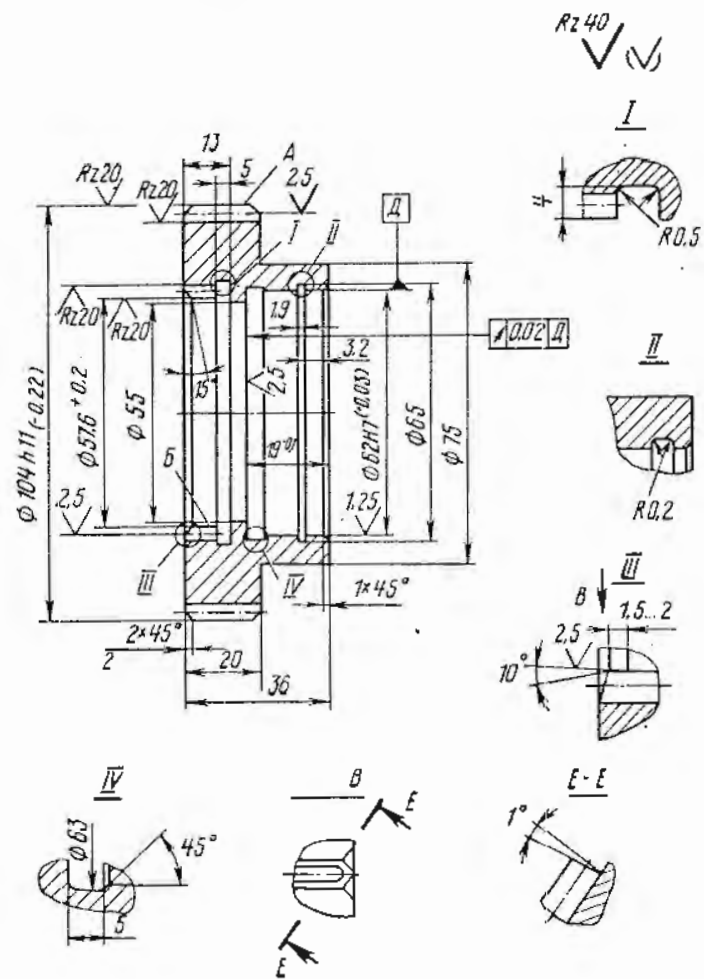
Колесо зубчатое, деталь № 3Л722А.322.403
